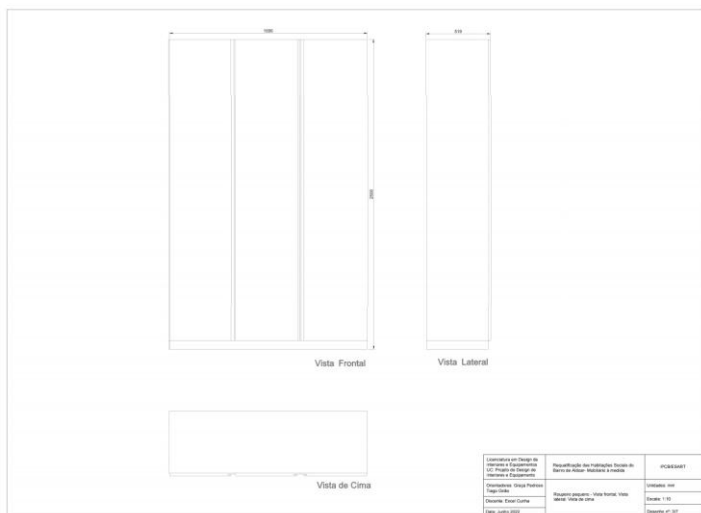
Desenho técnico de conjunto de vestuário 160cm
